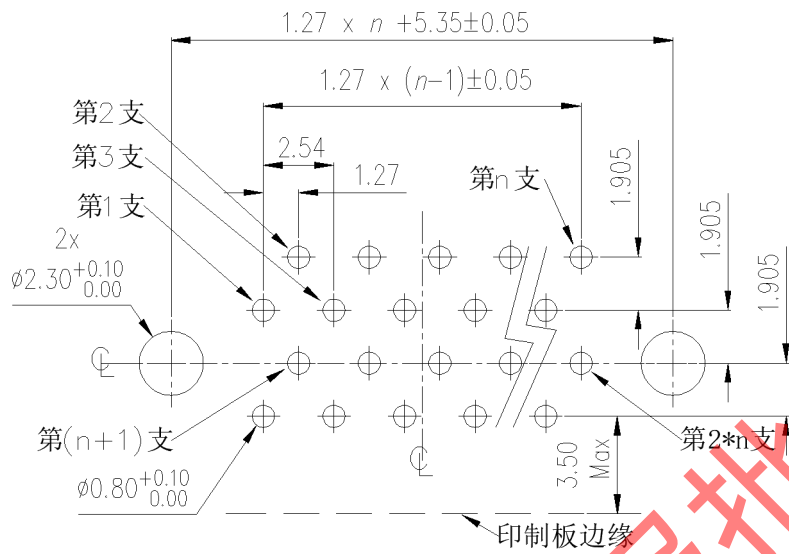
H 类型插座 90 度穿孔焊印制板开孔尺寸
